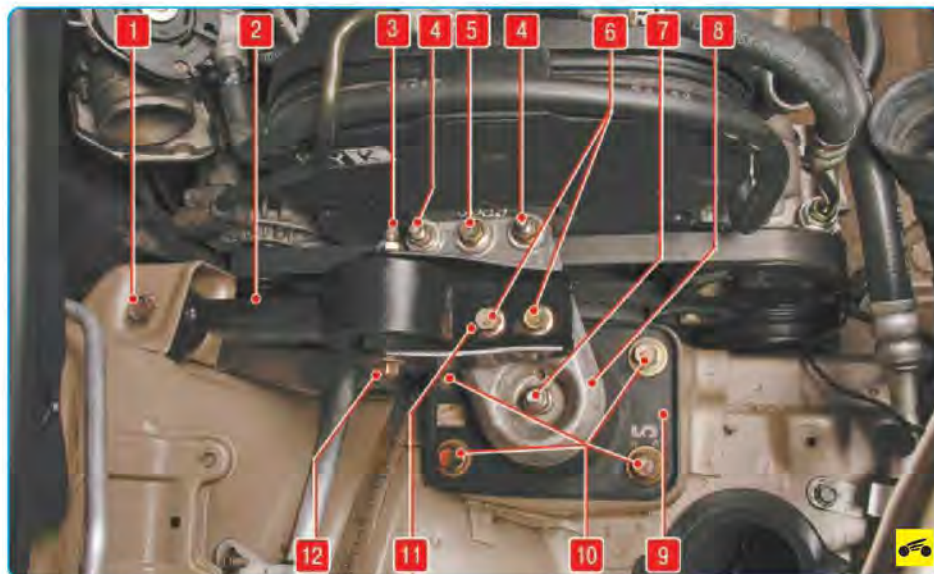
Правая опора подвески двигателя: 1 – болт крепления реактивной тяги к кронштейну кузова; 2 – реактивная тяга; 3 – гайка болта крепления кронштейна реактивной тяги; 4 – гайки шпилек кронштейна правой опоры; 5 – болт крепления кронштейна правой опоры; 6 – болты крепления кронштейна реактивной тяги к кронштейну правой опоры; 7 – гайка шпильки подушки правой опоры; 8 – кронштейн правой опоры; 9 – подушка правой опоры; 10 – болты крепления подушки правой опоры; 11 – кронштейн реактивной тяги; 12 – болт крепления кронштейна реактивной тяги
